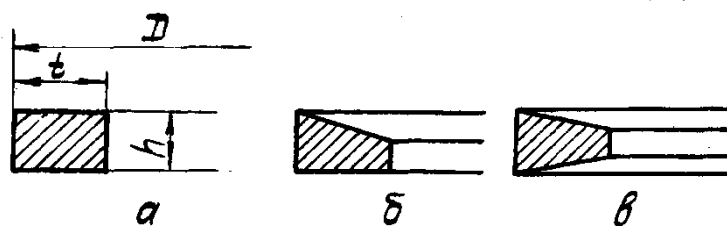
Профілі верхнього компресійного кільця:
